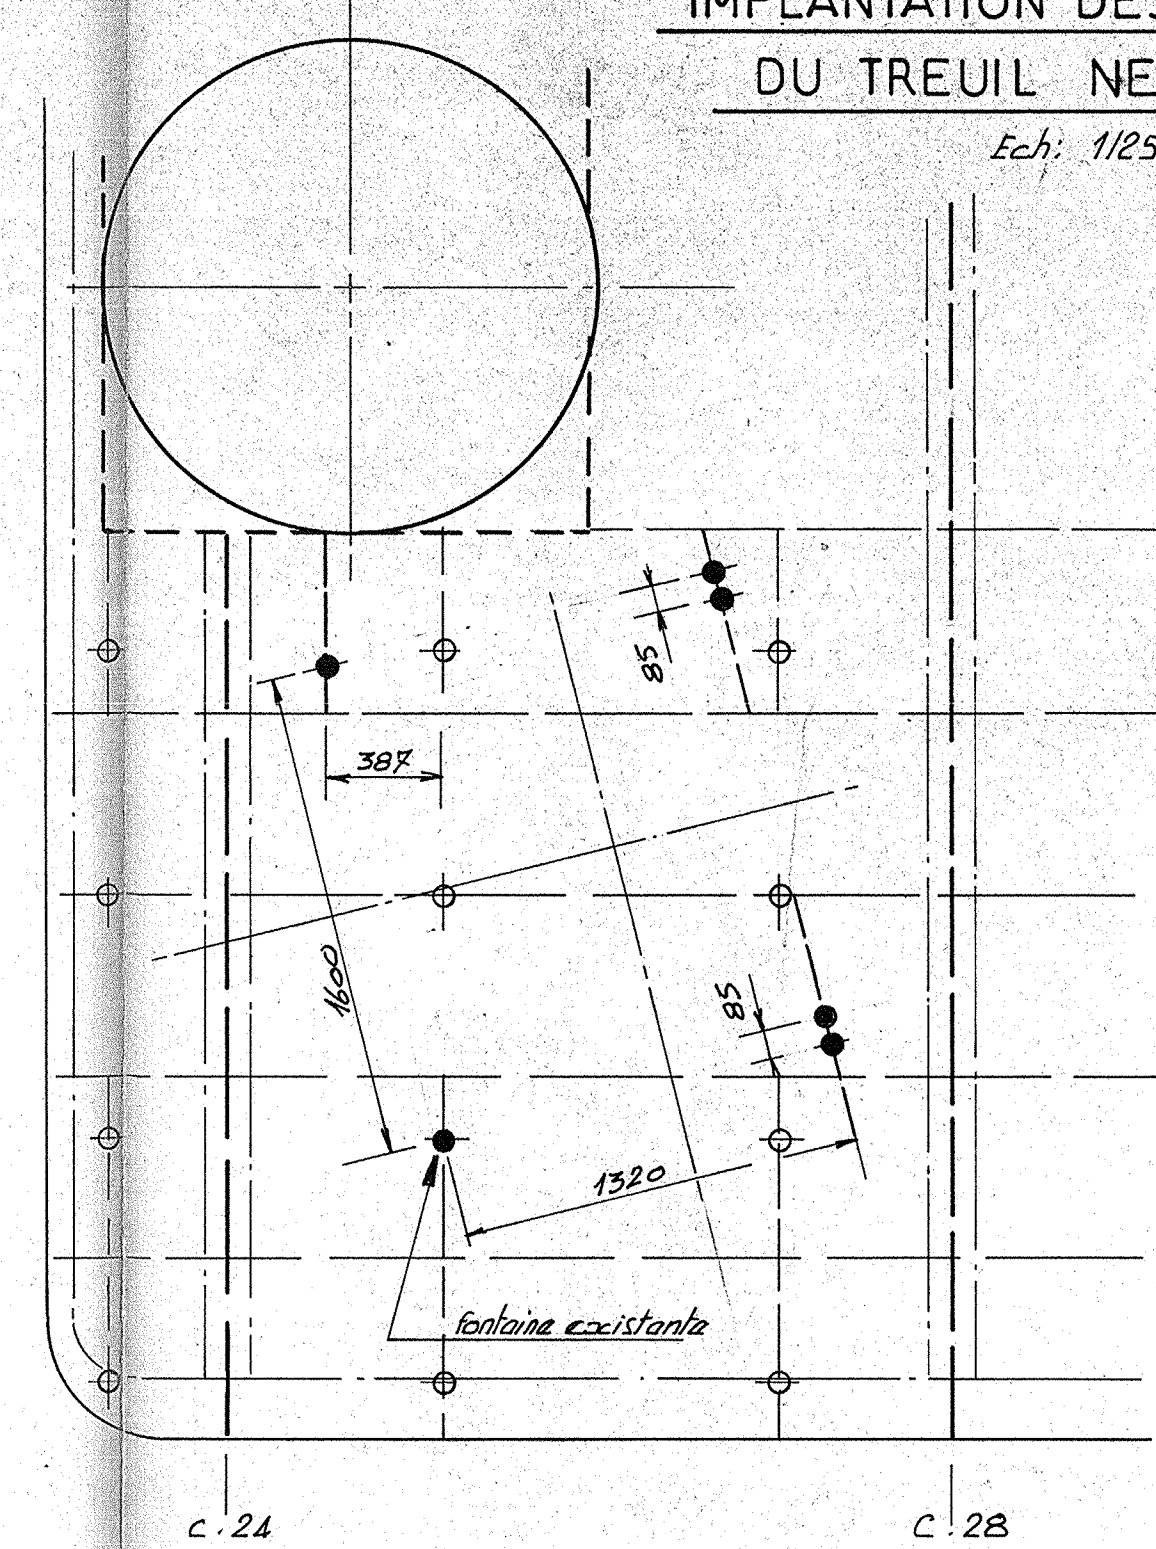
DETAIL D'IMPLANTATION DES FONTAINES AU PONT D
